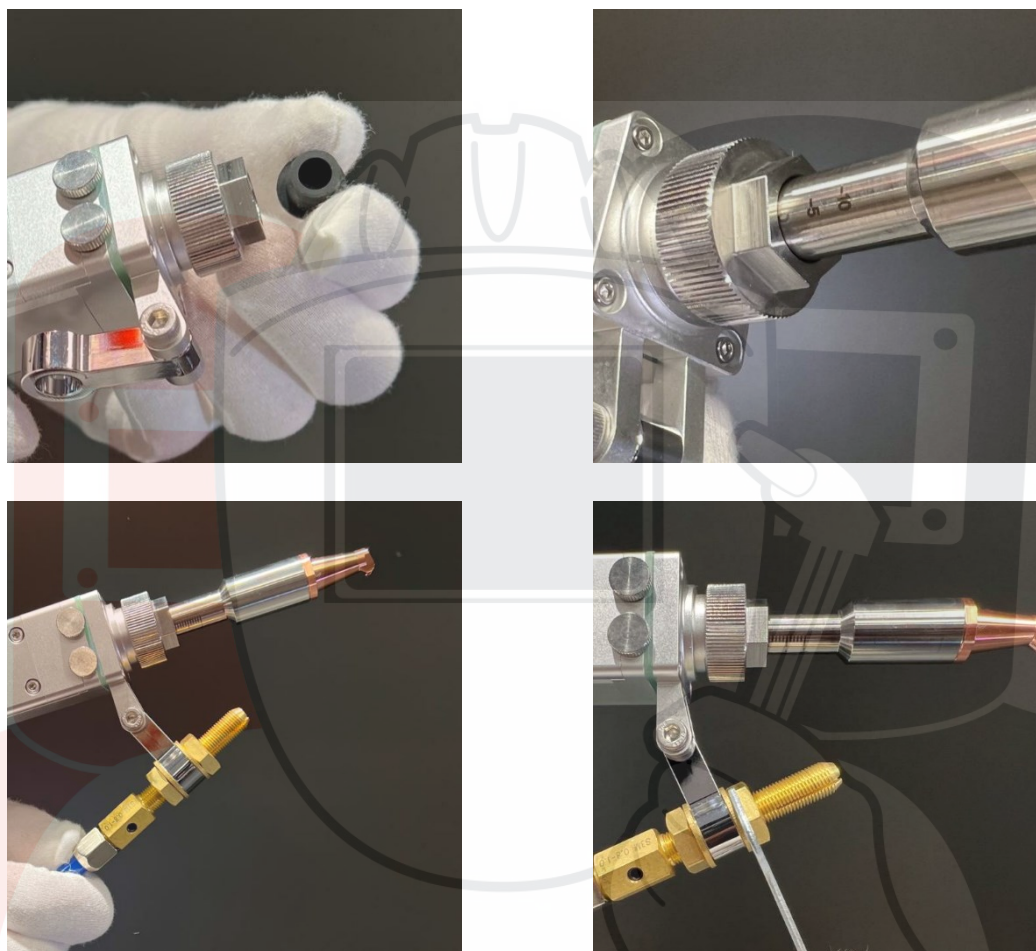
Выбор усилия зажатия сварочной проволоки.
